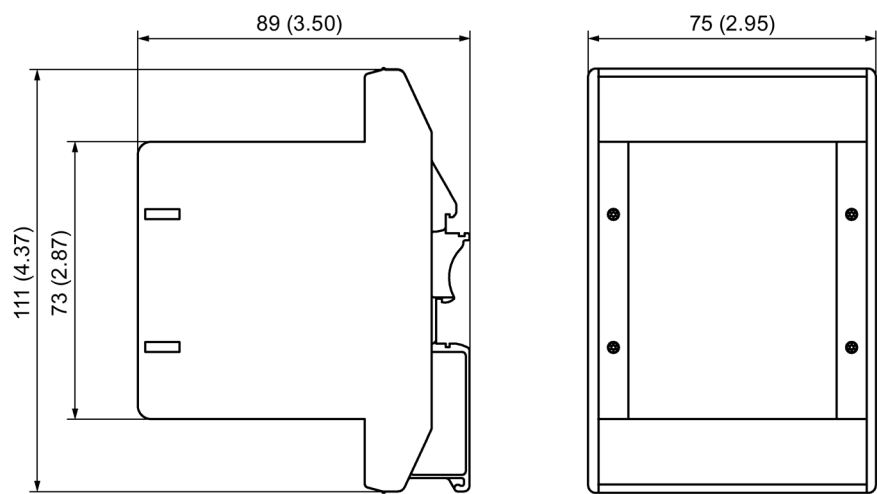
安全制动适配器的外形尺寸图，所有尺寸以毫米（尺寸）为单位
